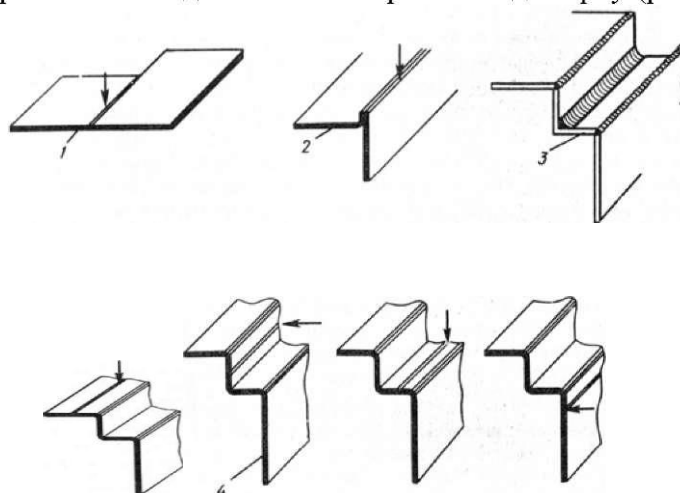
Подготовка кромок тонких листов под сварку: 1 - сварка встык; 2 - сварка с отбортовкой кромки; 3 - сварка внутренних или наружных углов не подвергается рихтовке; 4 - хорошее расположение сварочного шва, позволяющего производить рихтовку
